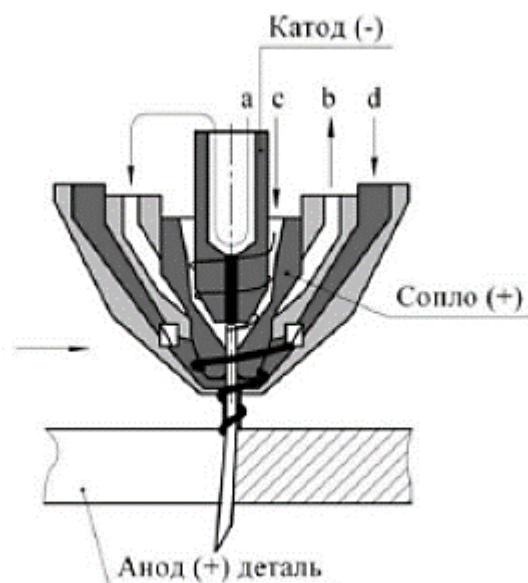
Конструктивная схема формирования тонкоструйной плазмы: а, б – каналы охлаждения катода и сопла; с – канал плазмообразующего газа; д – канал завихряющего газа
